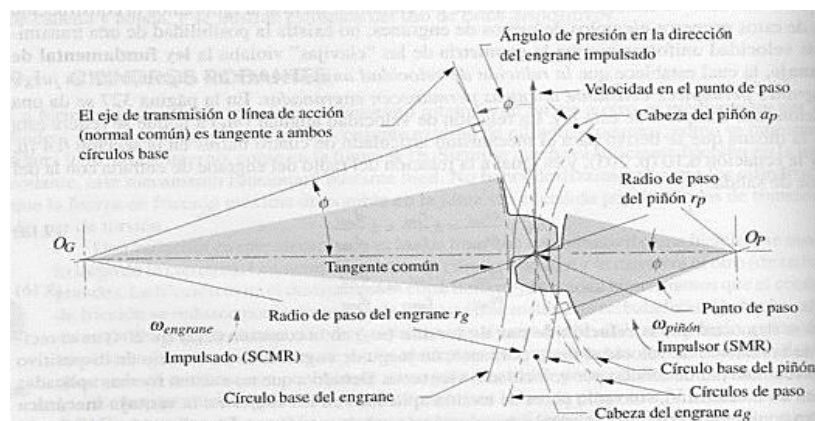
Geometría del contacto y ángulo de presión de dientes de engrane de involuta [2].
